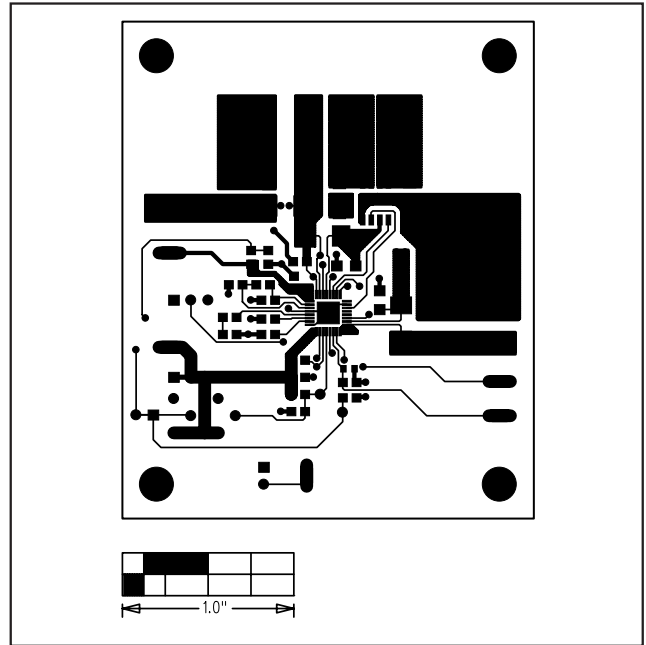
MAX1870A 评估板 PCB 布局图 — 元件面
